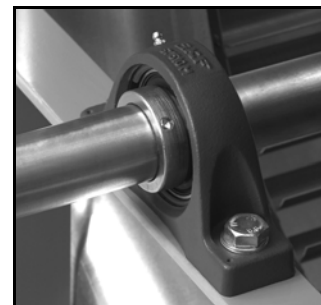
Pendelrollenlager / Rillenkugellager mit Steh-Gussgehäuse
